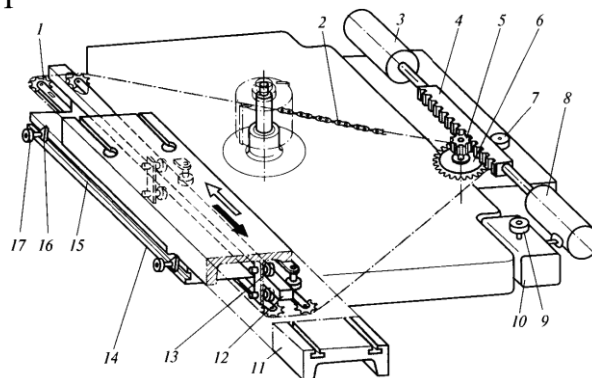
Привід каретки фрезерного верстата: 1, 6 – зірочки; 2 – ланцюг; 3 – пневмоциліндр; 4 – зубчаста рейка; 5 – шестерня; 7, 13 – опорні ролики; 8 – гідроциліндр; 9, 17 – ручки; 10 – бачок; 11 – каретка; 12 – напрямна; 14 – кронштейн; 15 – паз; 16 – упор
